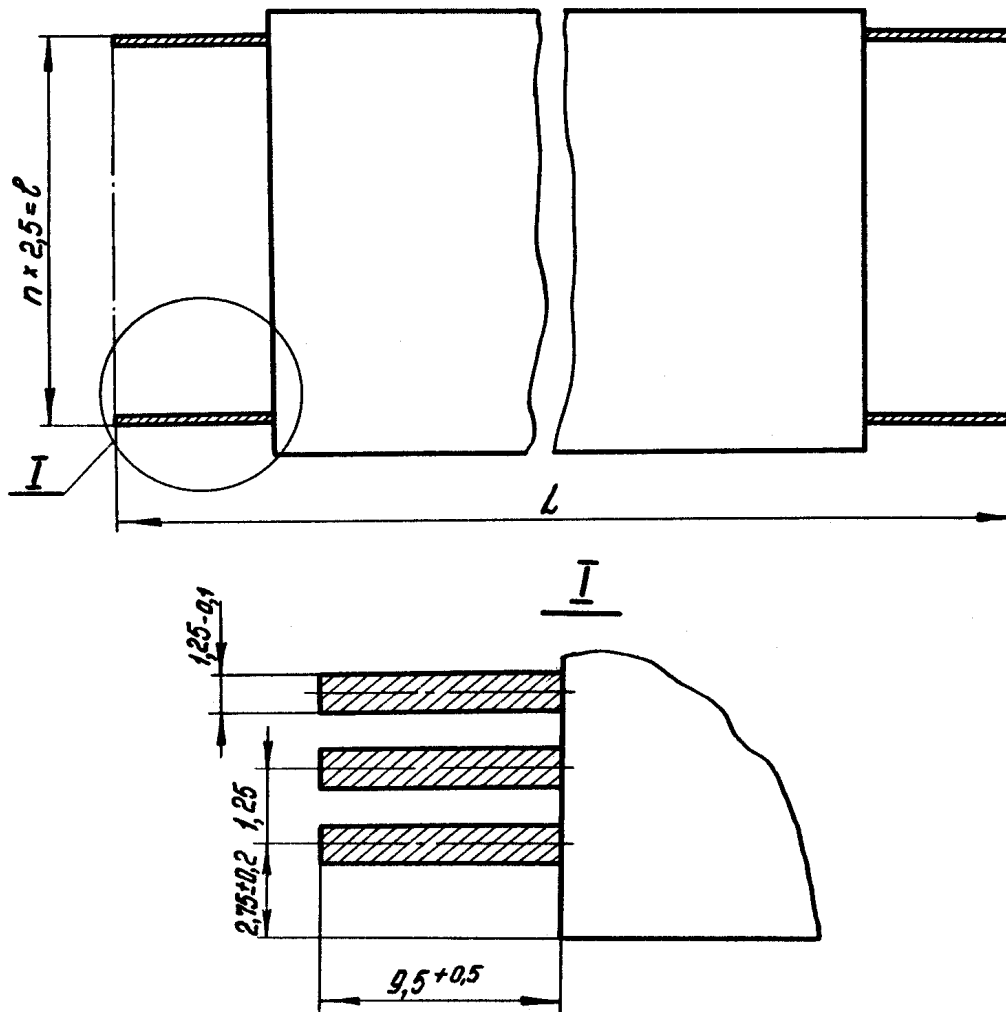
Гибкий печатный кабель с однорядными контактными лепестками одинаковой длины: L - длина кабеля (не более 348 мм); l - ширина кабеля (не более 57,5 мм)
